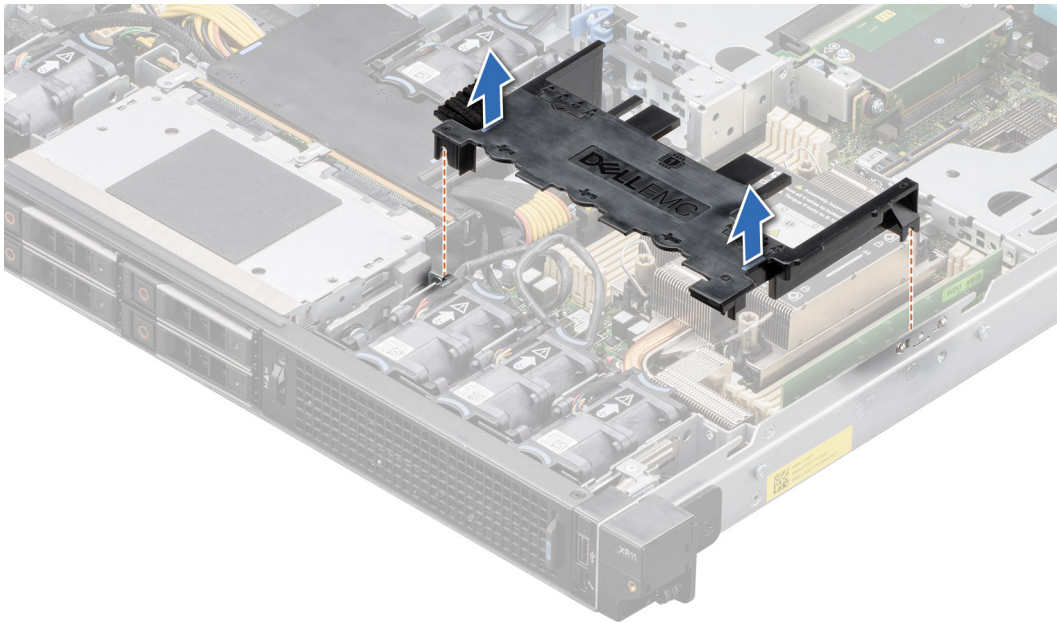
Entfernen des Prozessorkühlgehäuses
